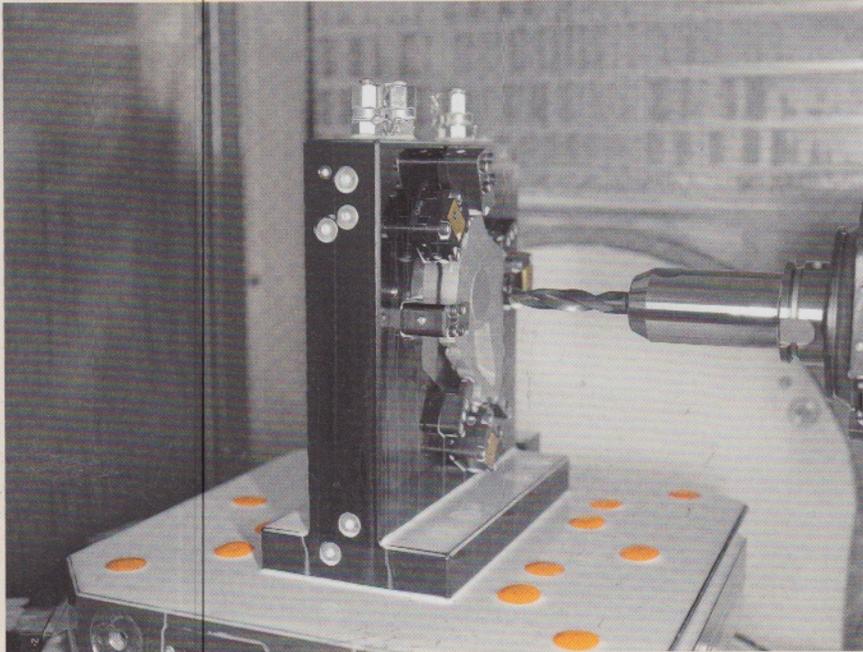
Die „Grob 350“ kann mit ihrem einzigartigen Maschinenkonzept der horizontalen Spindellage und dem Schwenktisch das Werkstück nach Messung der Lage für jede notwendige Bearbeitung toleranzgenau positionieren. Foto: AMF
